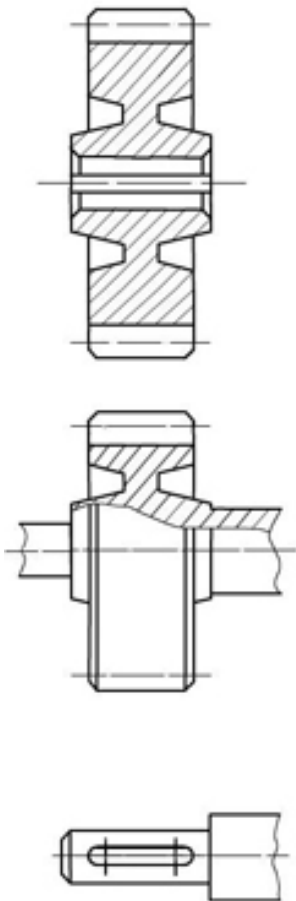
Зубчатая передача со шлицевым соединением в сборе
